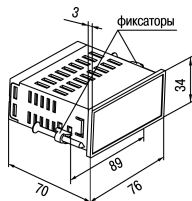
Габаритные размеры корпуса ЩЗ
